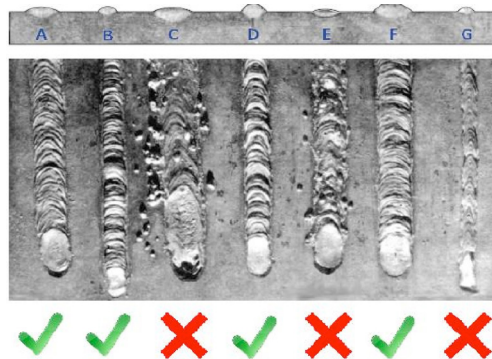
Pruebas de soldadura realizadas a diferentes velocidades y amperajes.
